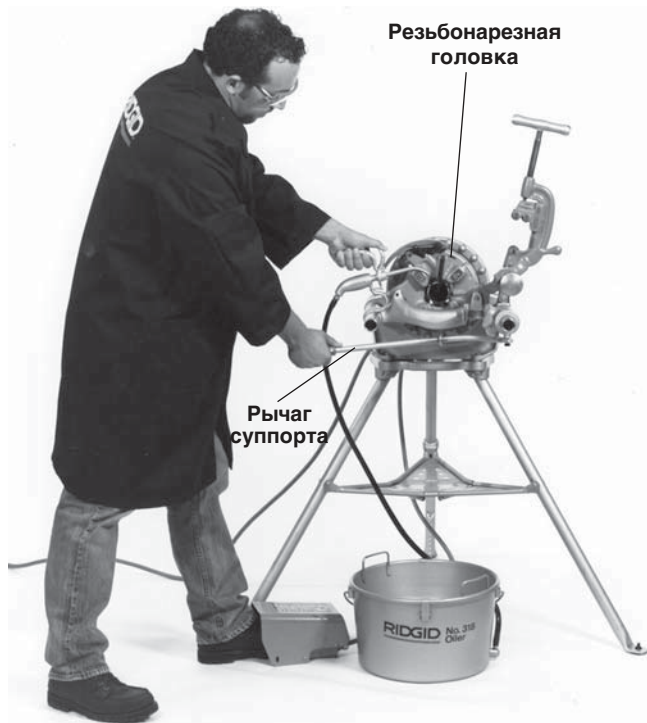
Нарезание трубной резьбы с помощью быстро- или самооткрывающейся резьбонарезной головки
